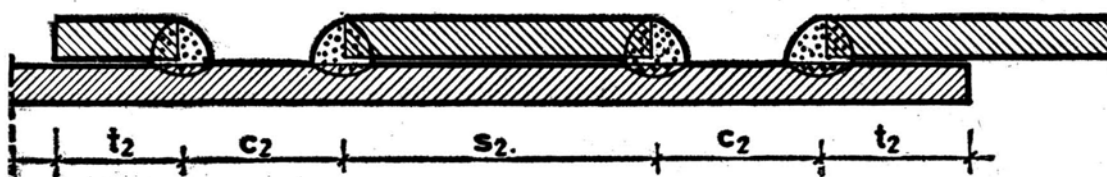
UNION CON SOLDADURAS DE RANURA
